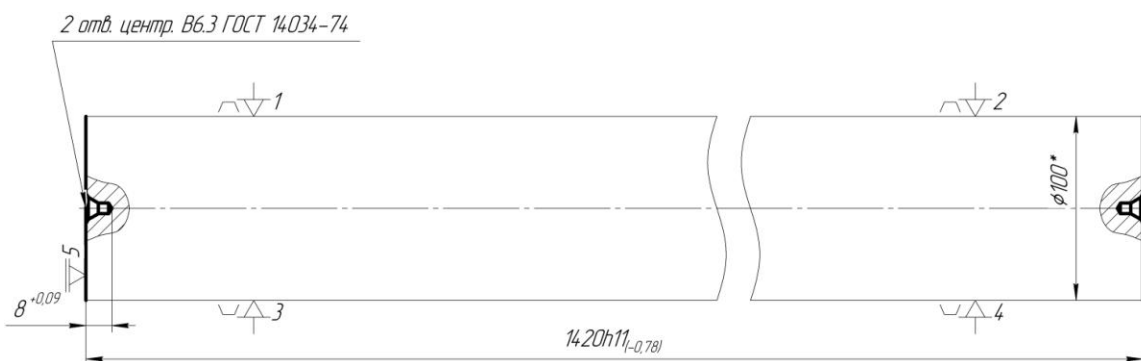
Схема установки заготовки в самоцентрувальні призми
